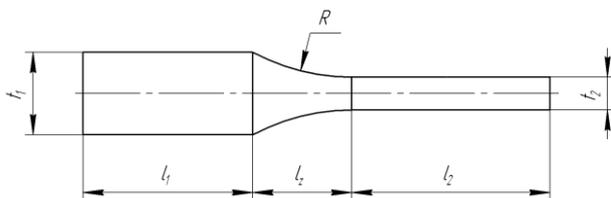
Профиль поперечного сечения сварочного инструмента
